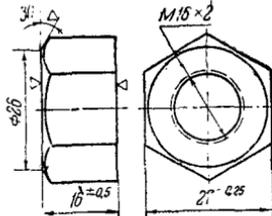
Дет. № 3037. Гайка к шпильке крепления всасывающей и выхлопной труб
